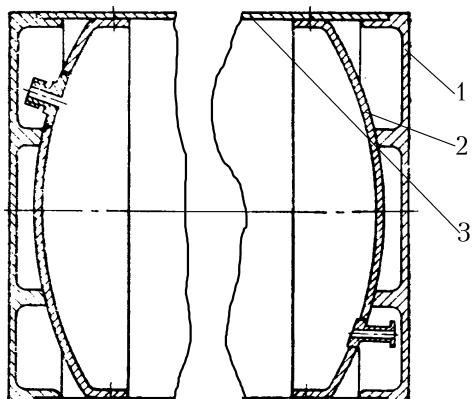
Конструкція паливного бака циліндричної форми:
